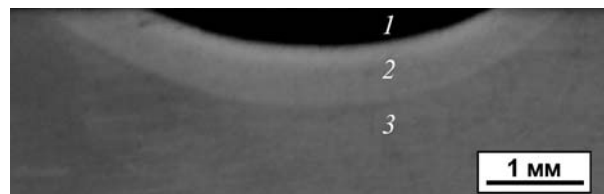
Макрошлиф поперечного сечения образца стали марки Р6М5 после лазерной закалки с оплавлением поверхности
